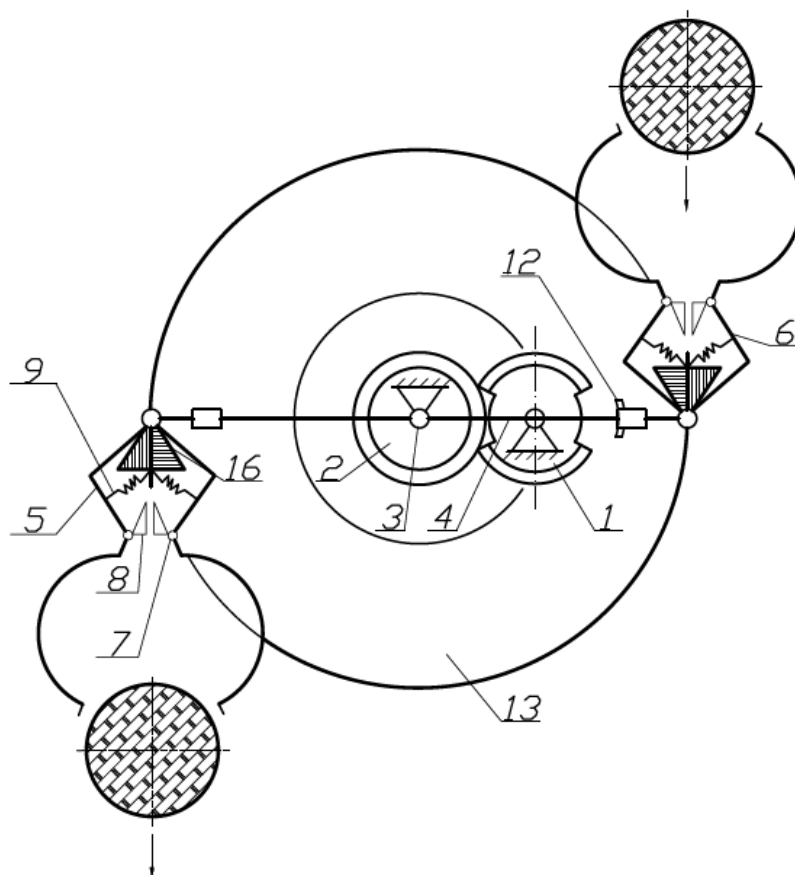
Схема манипулятора для передачи изделий с выстоем рабочего органа
